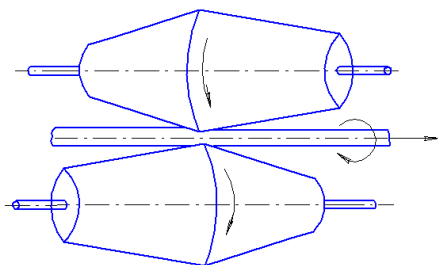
Схема клетки с косо или наклонно расположенными валками
